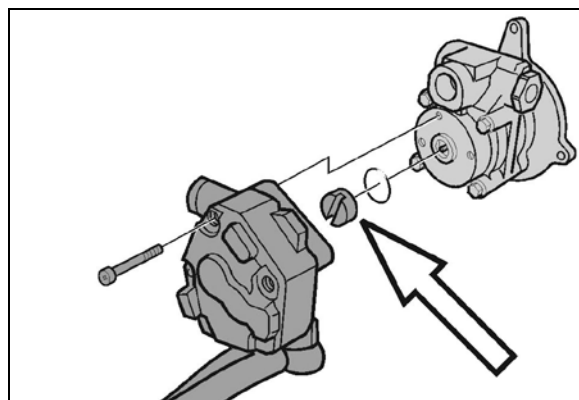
ARBRE D'ENTRAÎNEMENT DE LA POMPE À CARBURANT
